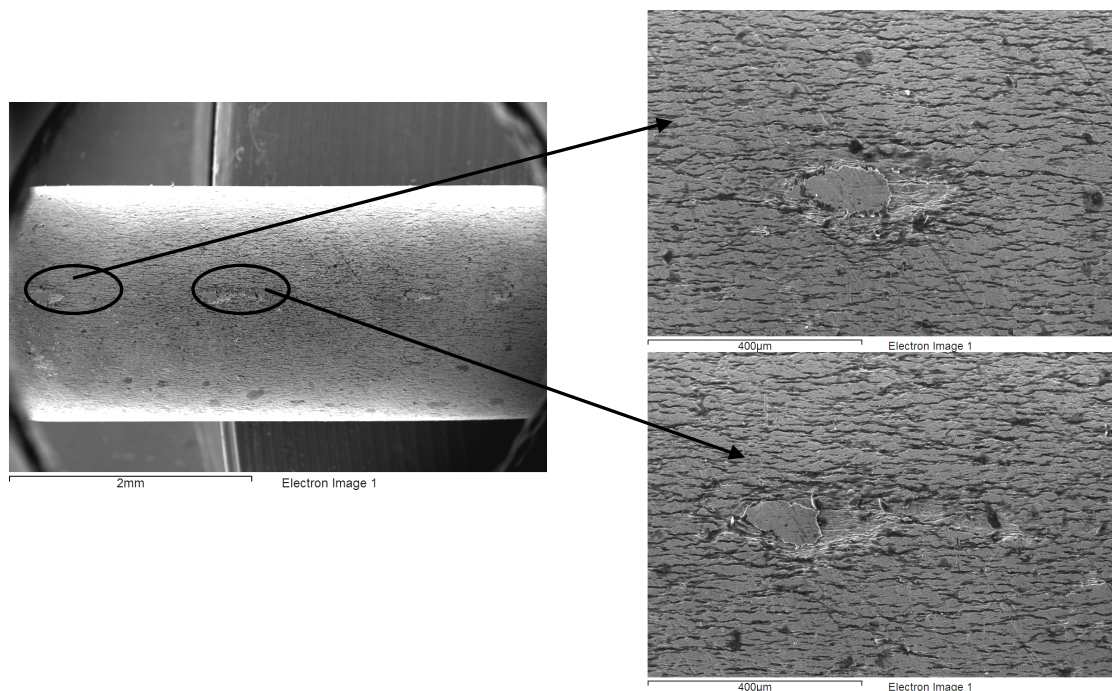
Вид дефектов, обнаруживаемых на поверхности капиллярных труб и являющихся закатанными мелкими частицами металлов либо трубы, либо деформирующего инструмента
